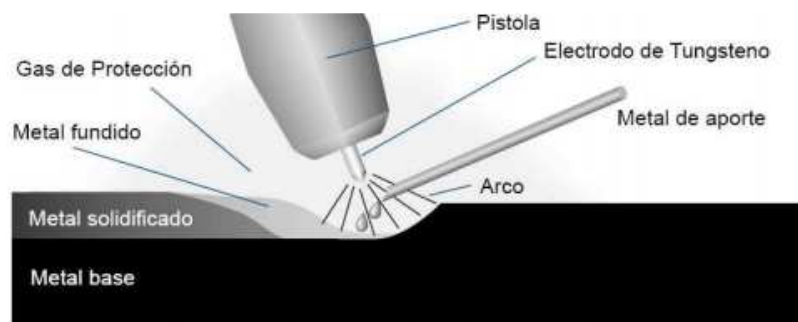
Diagrama Esquemático del Proceso de Soldadura GTAW³⁵
